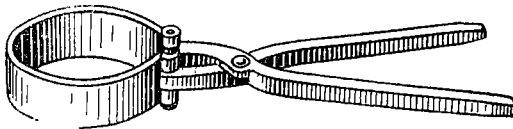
Приспособление для установки поршня с кольцами в цилиндр двигателя
